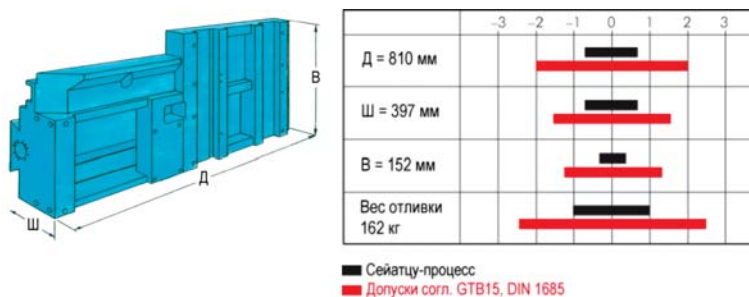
Допуски по корпусным деталям при изготовлении по Сейатцу–процессу
